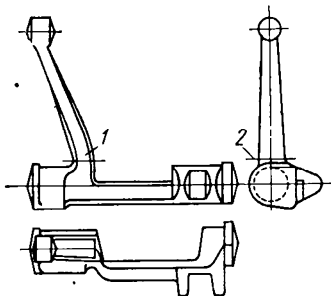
Поковка, состоящая из поковок для двух деталей: 1 и 2 — линии, по которым при ином варианте штамповки производилась сварка
